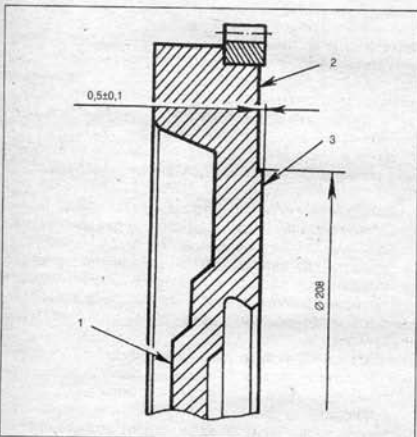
Маховик: 1 - поверхность, прилегающая к фланцу коленчатого вала; 2 - место проверки поверхности для крепления сцепления; 3 - место проверки биения опорной поверхности ведомого диска сцепления
